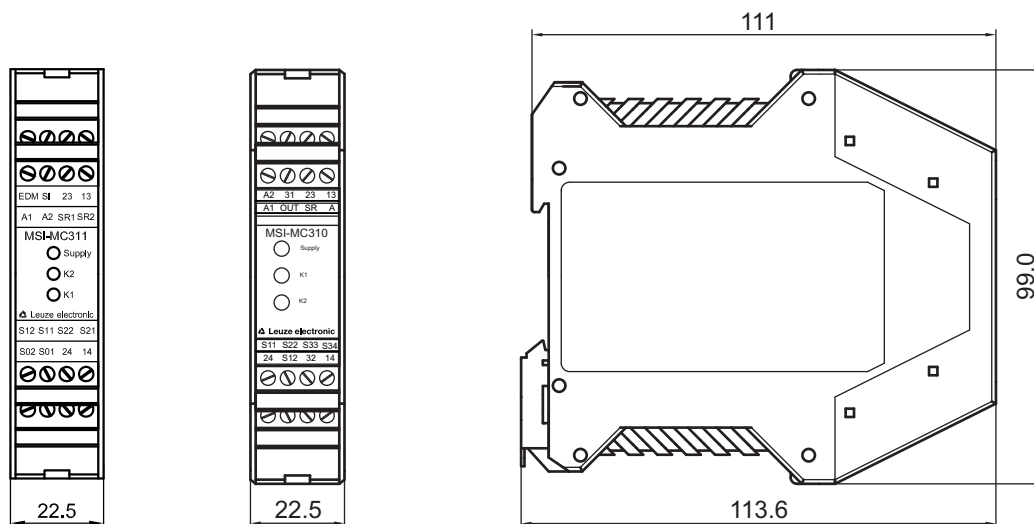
Dimensioni modulo di sicurezza MSI-MC310/MSI-MC311
